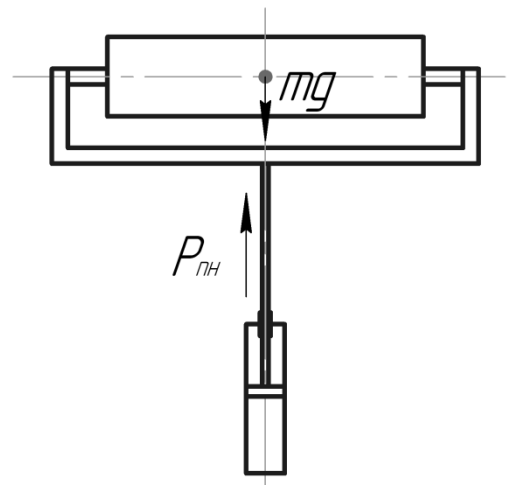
Розрахункова схема для підбору пневмоциліндра упора
